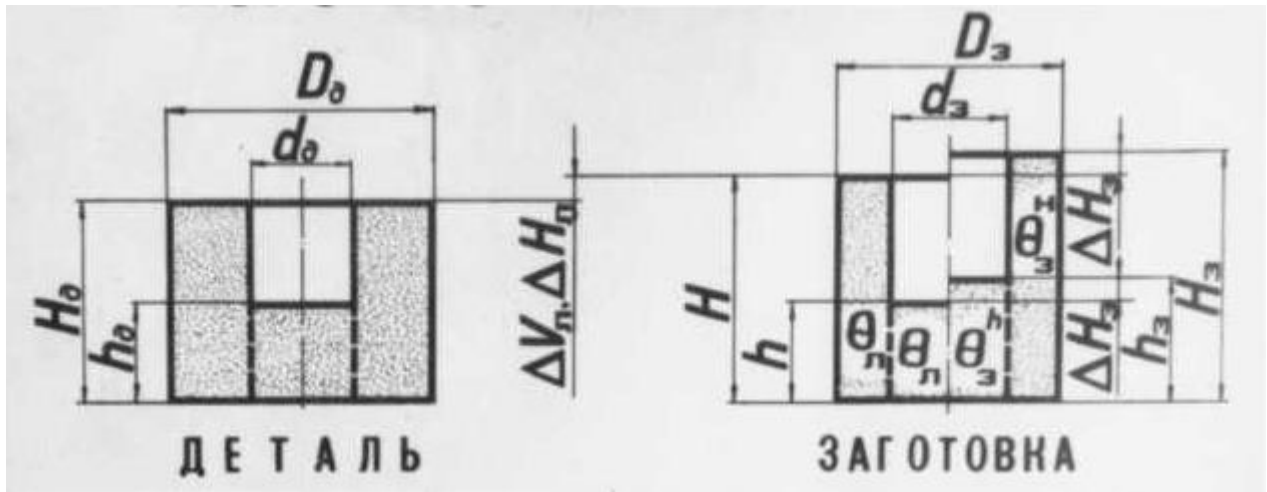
Деталь і заготовка з різними по висоті ділянками.
